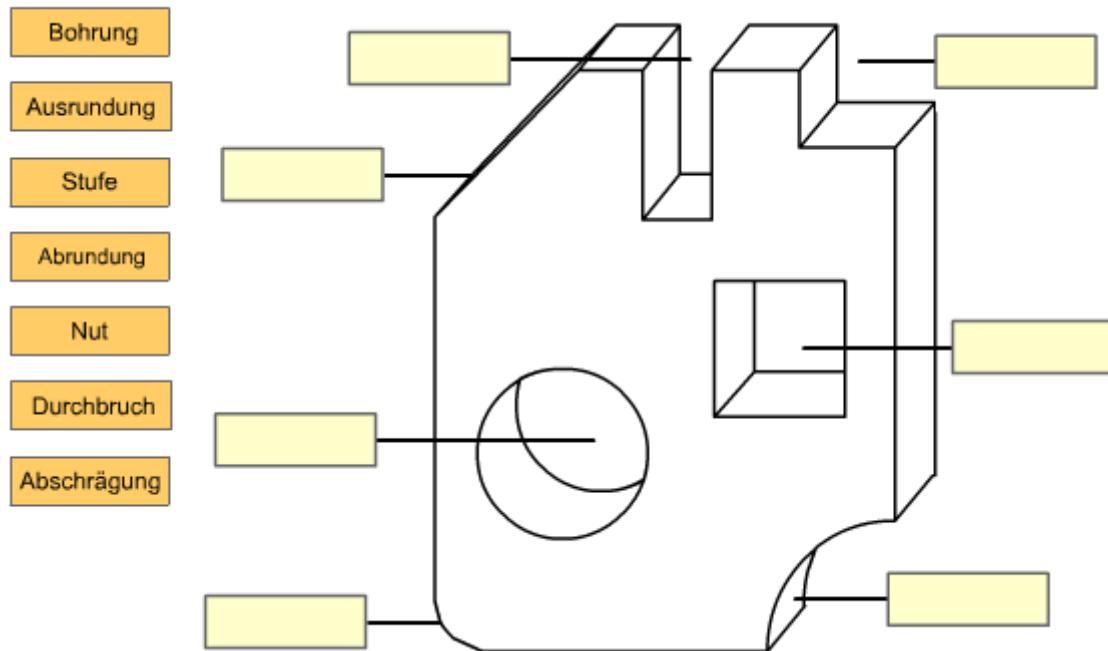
Werkstück - mehrfach bearbeitet
